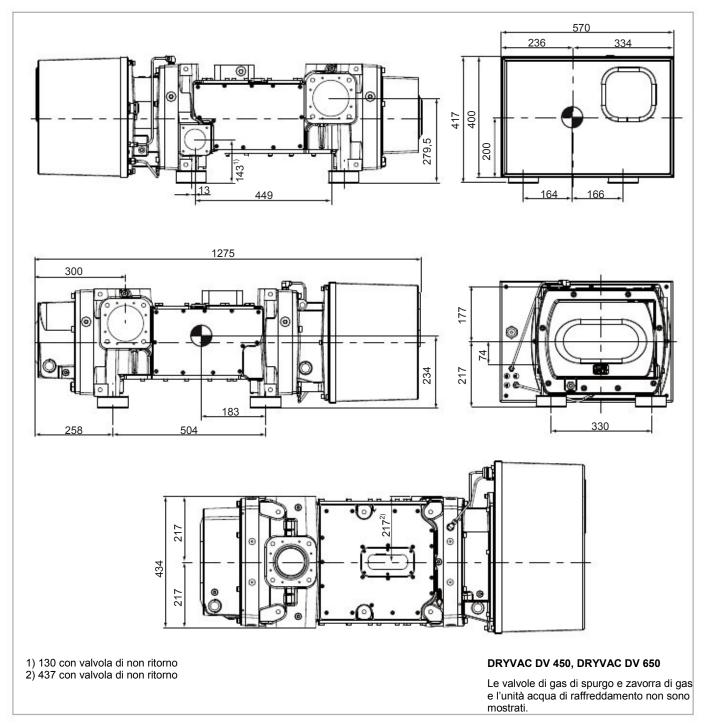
Disegno dimensionale, dimensioni in mm
